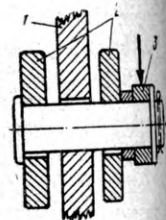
Схема приложения сил на валик шарнирного соединения тормозного башмака с подвеской
